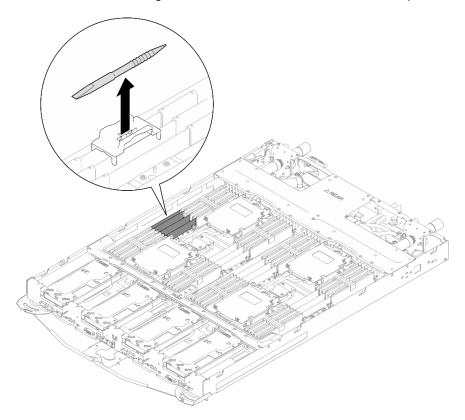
Entfernen des Speichermodul-Werkzeugs
